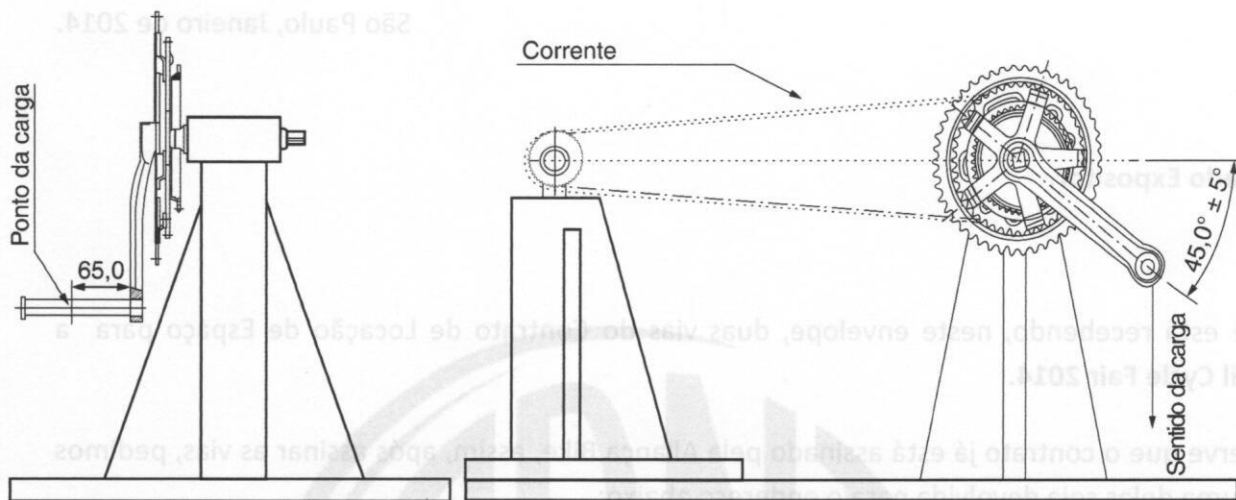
Equipamento de ensaio da pedivela montado com engrenagem com carga dinâmica
